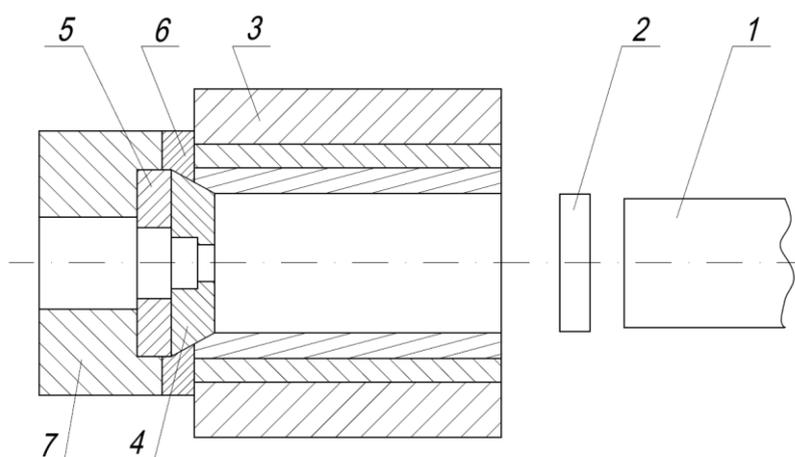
Инструментальная наладка для прессования прутков прямым методом: 1- прессштемпель; 2- пресс-шайба; 3- контейнер; 4- матрица; 5- подкладка; 6- крышка матрицедержателя; 7 – матрицедержатель.
